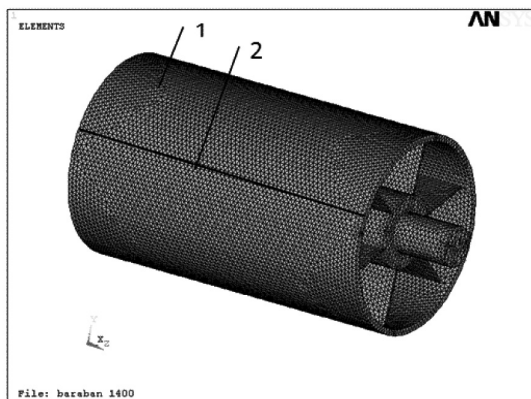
Модель барабана ленточного конвейера: 1 – обечайка, 2 – сварной шов
